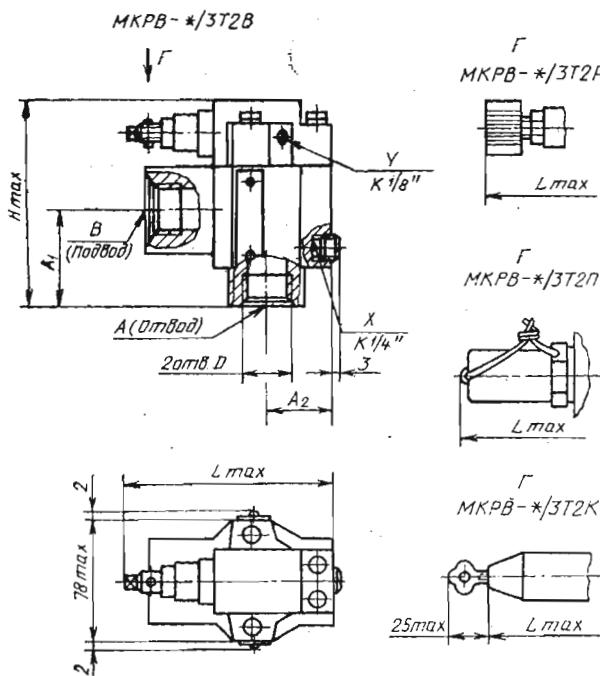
Габаритные и присоединительные размеры гидроклапанов редукционных трубного монтажа типа МКРВ-*/3Т2
